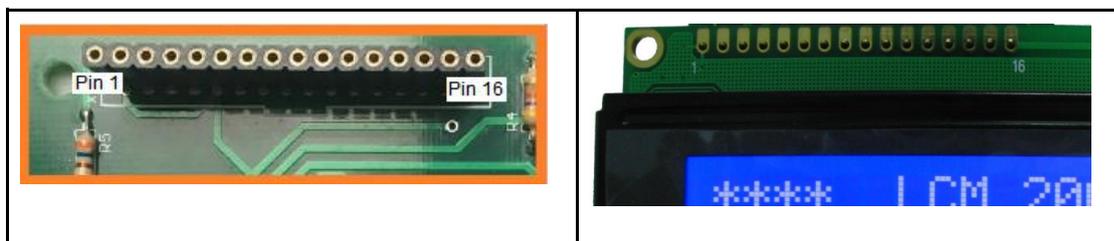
ESQUEMA DE ENSAMBLADO DE PANTALLA
